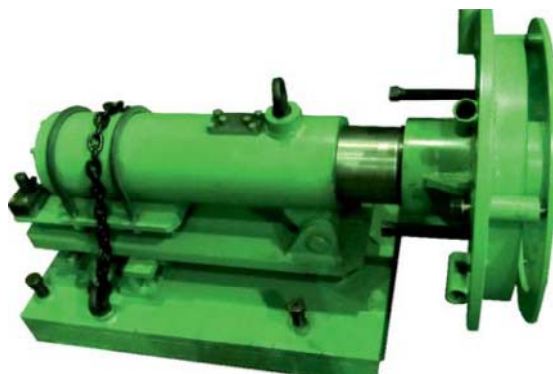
Приспособление для демонтажа-монтажа водил первого ряда и крышки редуктора мотор-колеса
